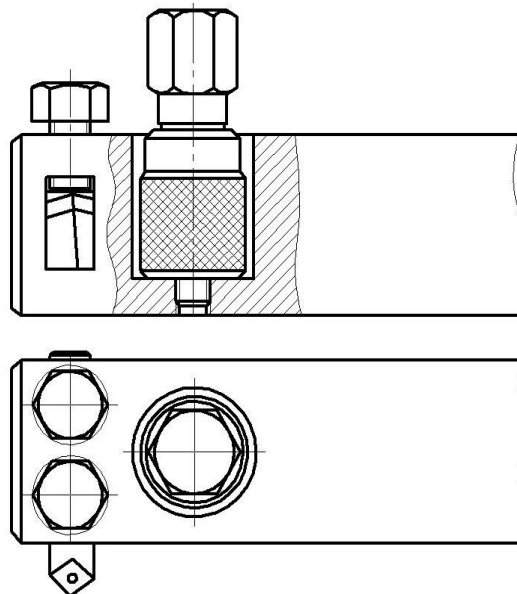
Виброгаситель Д. И. Рыжова, установленный в корпусе расточной оправки
